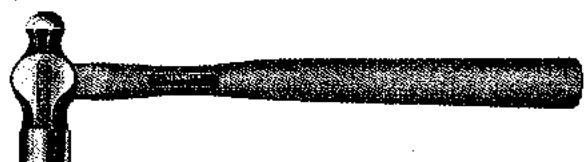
Martillo de punta de bola (Stanley Tools).
